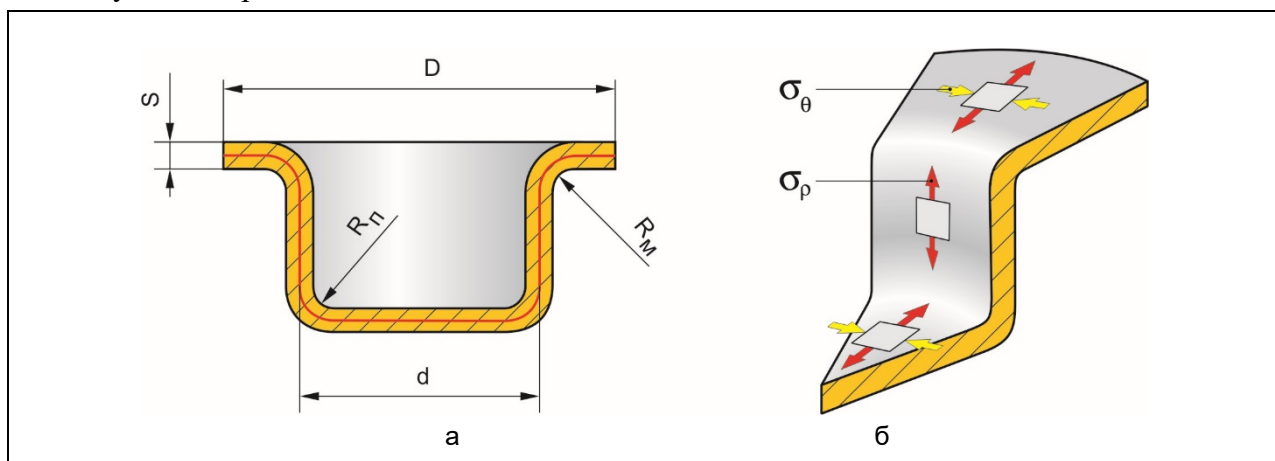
Обозначение размеров заготовок и напряжения, действующие в них.
